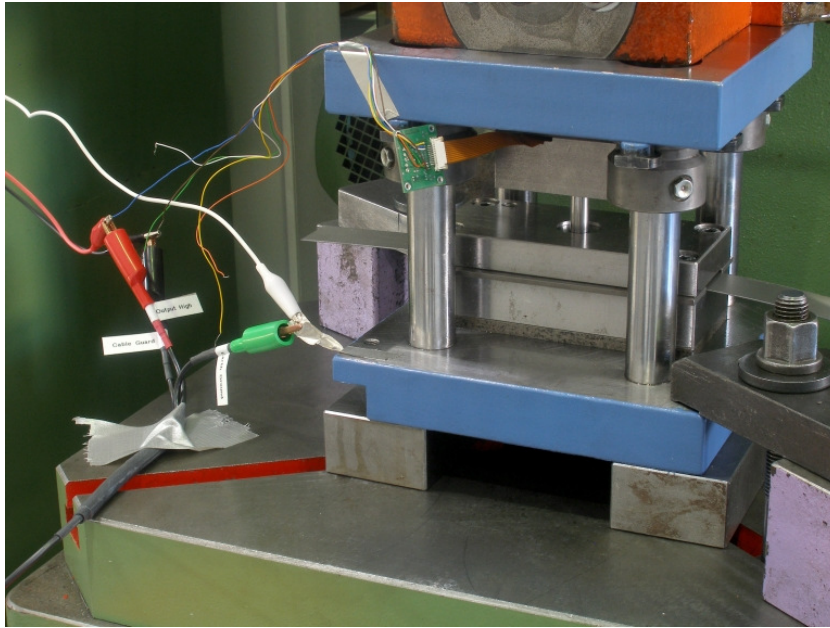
Lochwerkzeug mit Stempel für Durchmesser 10 mm
